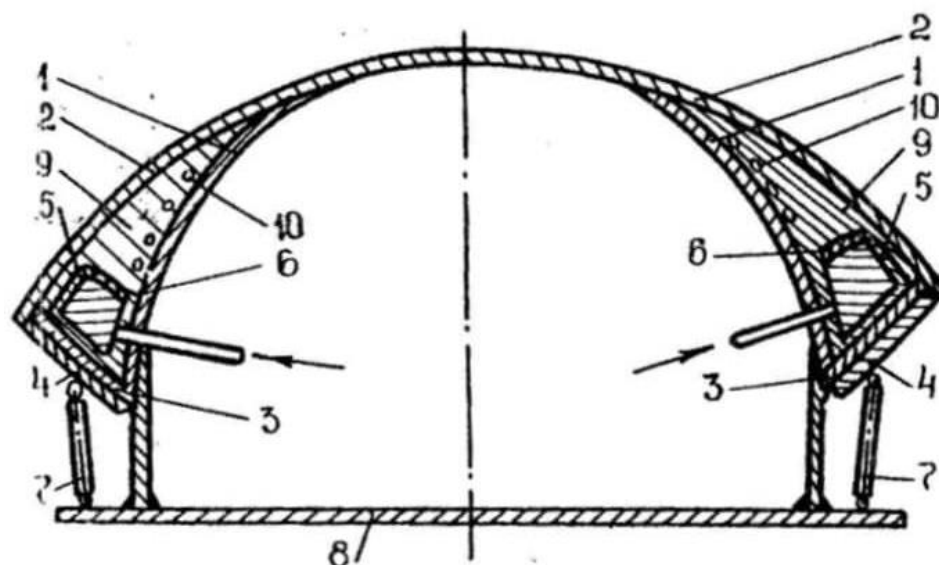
Пуансон с регулируемой рабочей поверхностью: 1- корпус; 2 – упругая оболочка; 3 – направляющие; 4- стенки оболочки; 5 – металлические резервуары; 6 – эластичные диафрагмы; 7 – силовые элементы; 8 – основания пуансона; 9 – наполнитель; 10 – нагревательный элемент
